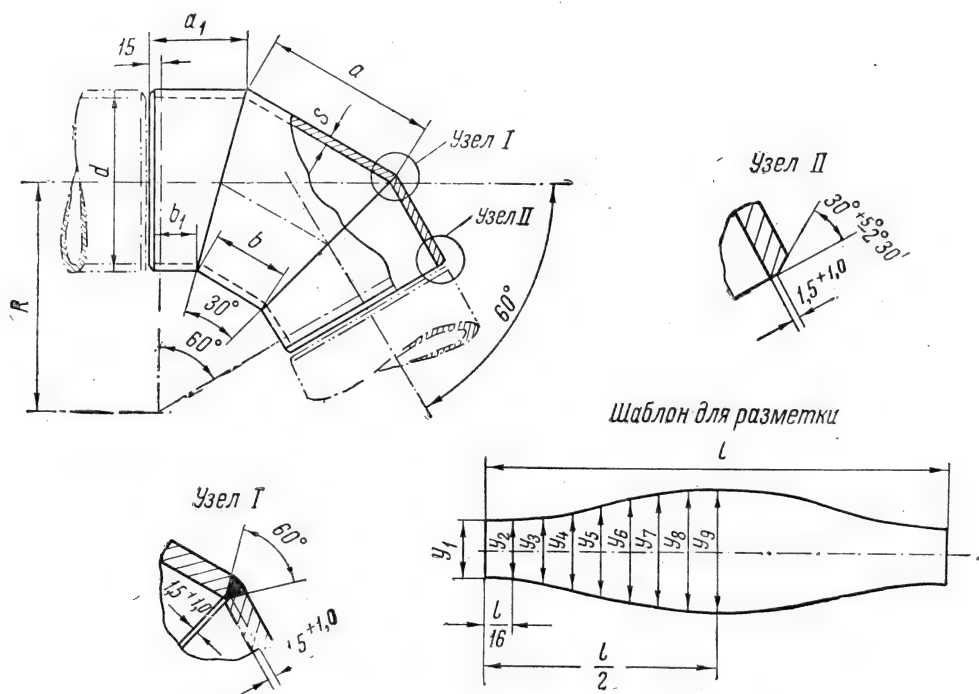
Отвод сварной с углом поворота 60° .
